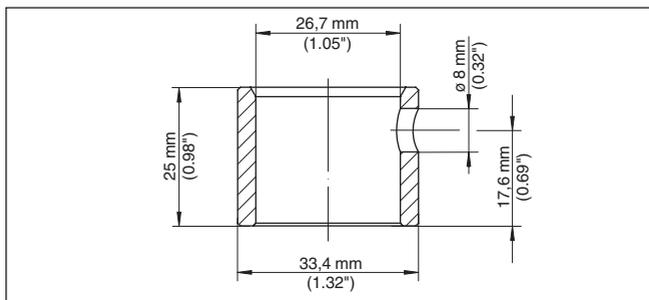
Dimensiones racor para soldar PMC 1" - VEGABAR 82
